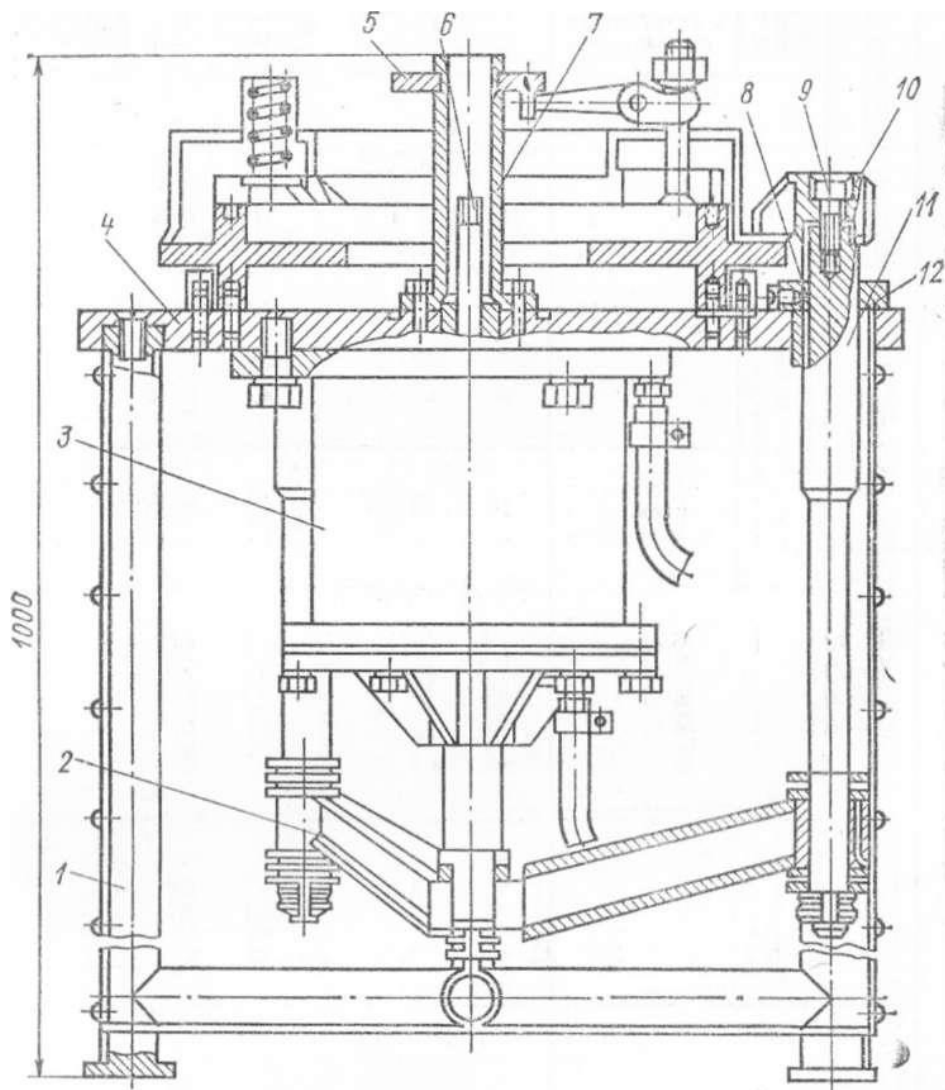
Стенд для розбирання муфти зчеплення ОПР-2827 (аналог): 1 – стендова рама; 3 – пневмоциліндр; 2 – хрестовина; 5 – шайба регулювальна; 4 – плита; 7 – втулка фланцева; 6 – шток; 8, 9 – гвинти; 11 – тяга; 10 – кулачок; 12 – втулка [2].
